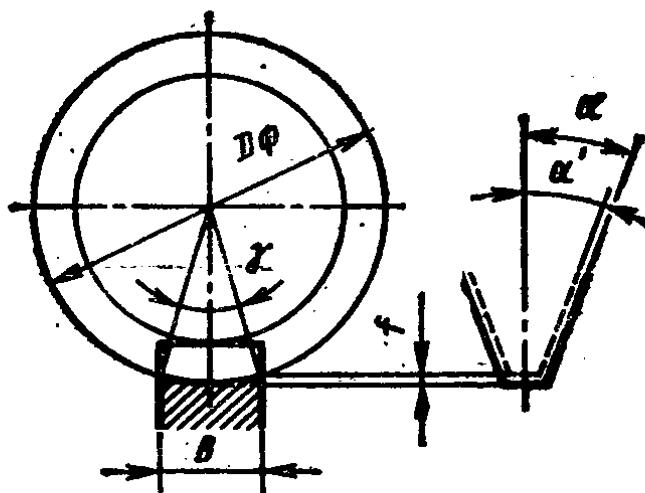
径向进给切削时齿根凹面圆弧高度 f 的计算
